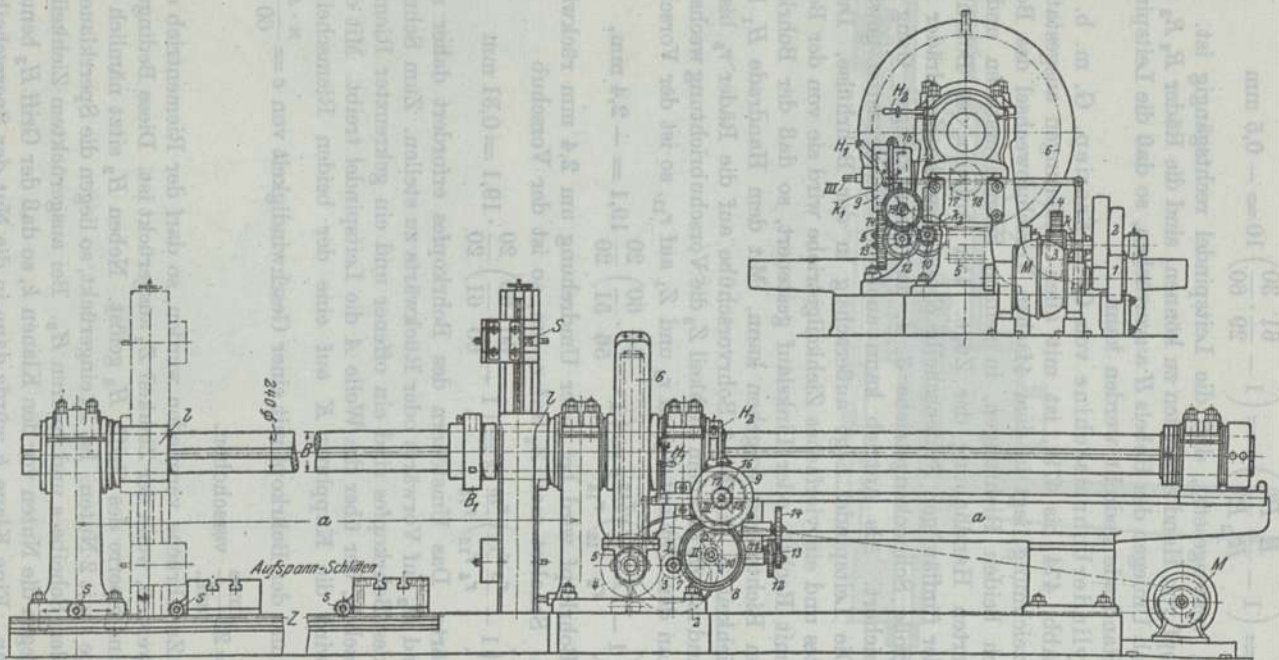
und 481. Zylinderbohrmaschine mit wandernder Bohrstange von Collet & Engelhard, Offenbach.
